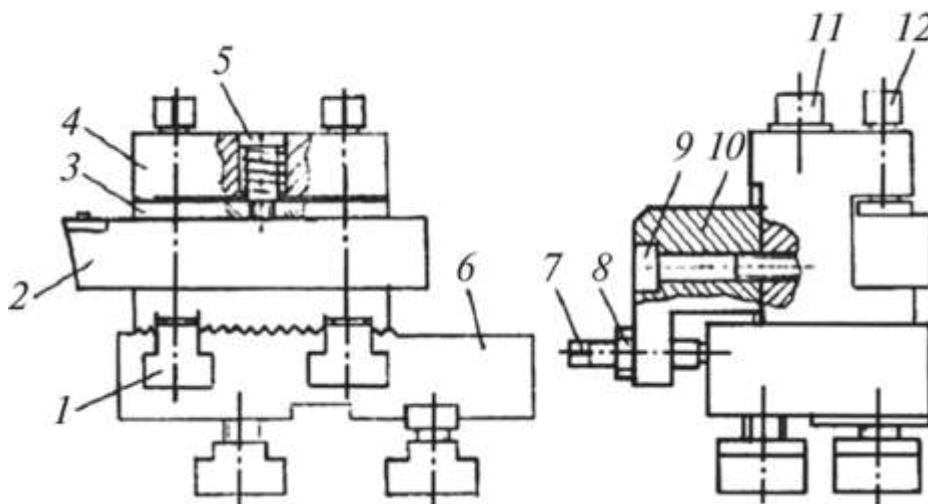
Схема швидкозмінних різцевих державок
